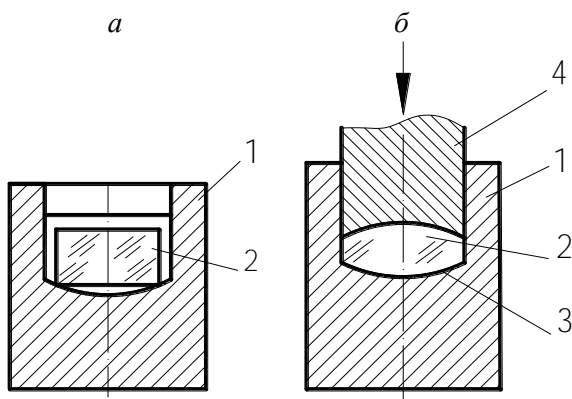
Схема получения заготовок стеклянных линз прессованием
